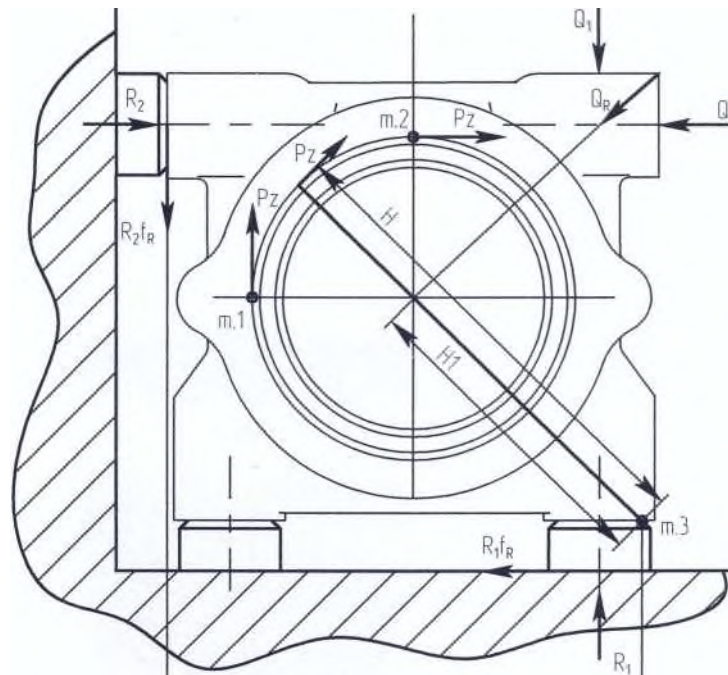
Розрахункова схема закріплення заготовки
